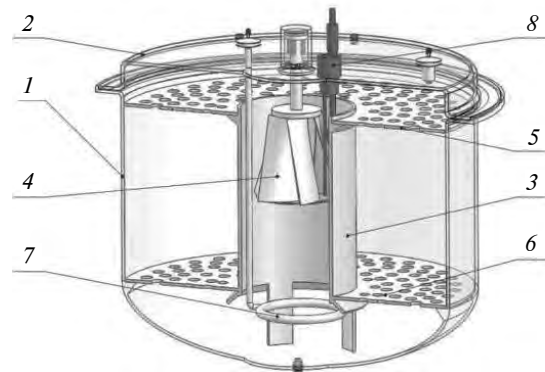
Конструкція ферментера/біореактора: 1 – корпус; 2 – кришка; 3 – циркуляційна труба; 4 – перемішувальний пристрій V-blade; 5 – верхня решітка; 6 – нижня решітка; 7 – барботер; 8 – датчики контролю
